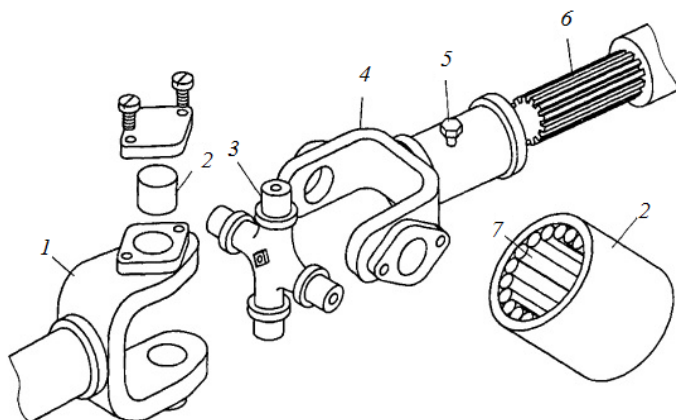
Детали карданного шарнира неравных угловых скоростей: 1, 4 – вилки; 2 – корпус подшипника; 3 – крестовина; 5 – масленка; 6 – шлицевое соединение; 7 – игольчатые подшипники
